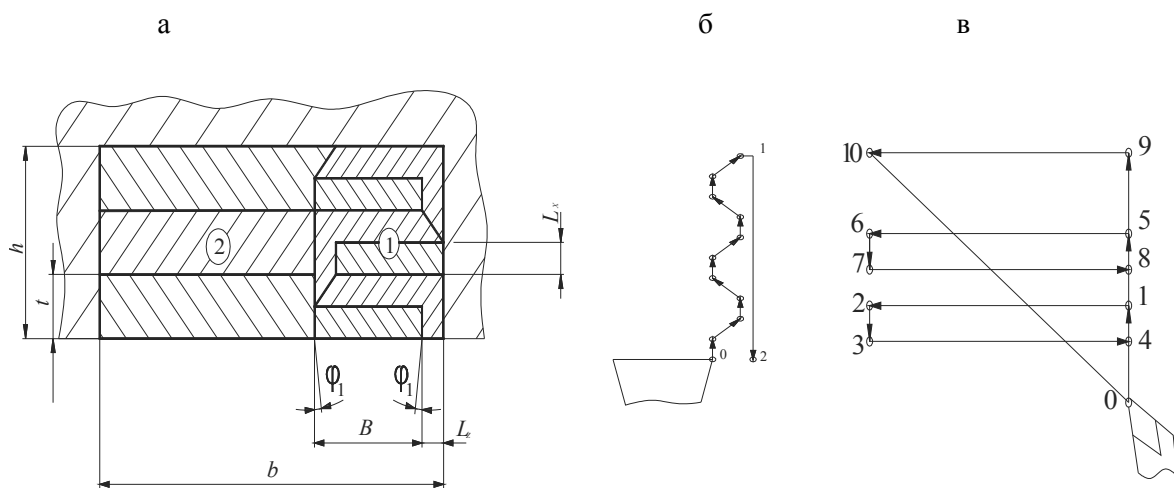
Схема (а) и циклы (б,в) обработки закрытой поверхности вращения (канавки или проточки) прорезным и подрезным резцами
